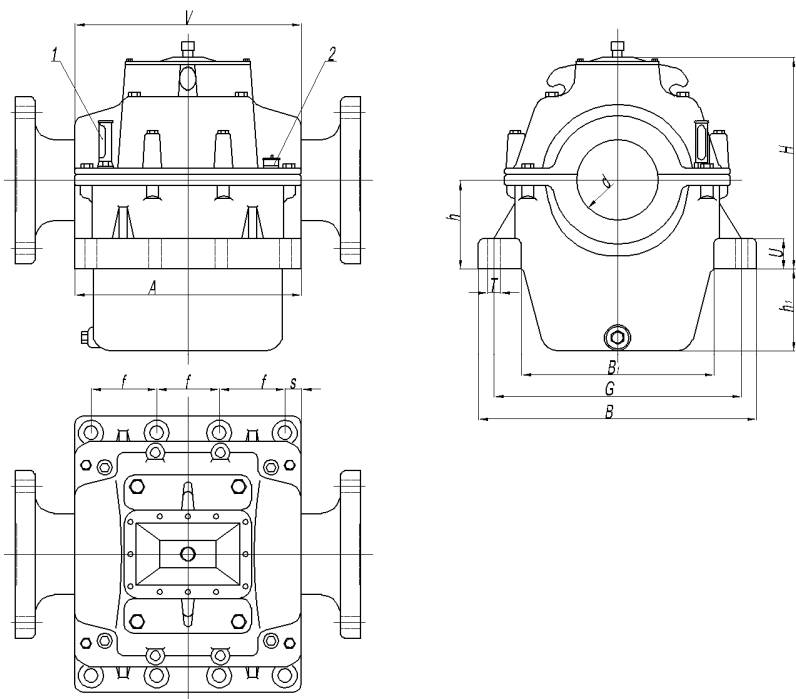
Корпус упорно-опорного подшипника: 1 – термометр масла; 2 – указатель уровня масла
